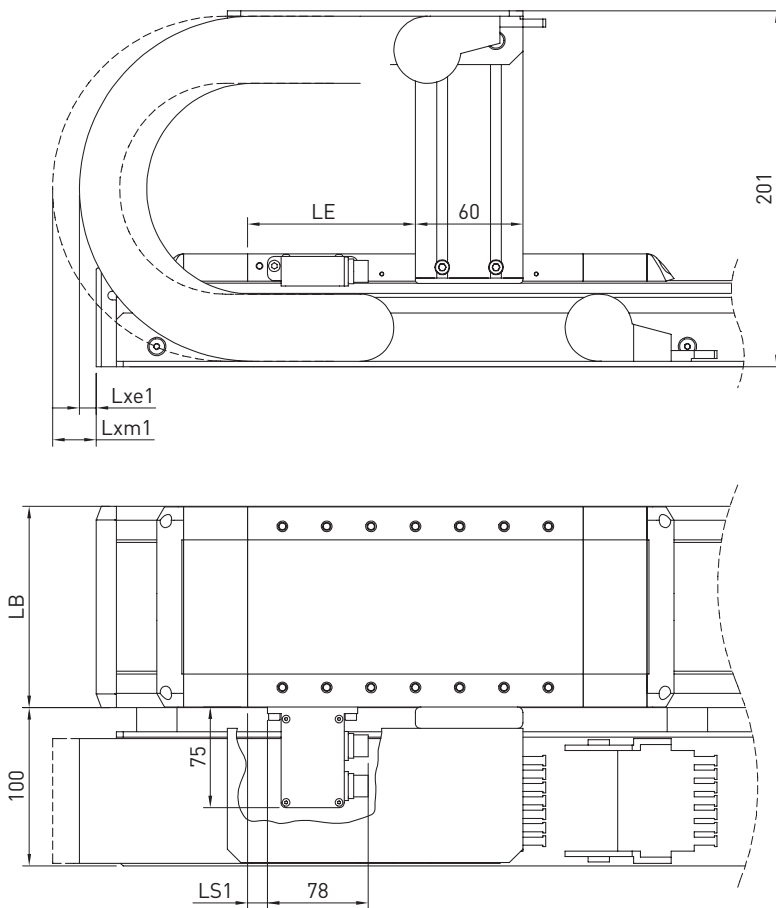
Linearmotorachsen HT100L: Option „D“ und „F“ – Stecker rechts/hinten, gilt gespiegelt auch für Option „C“ und „E“ – Stecker links/hinten
